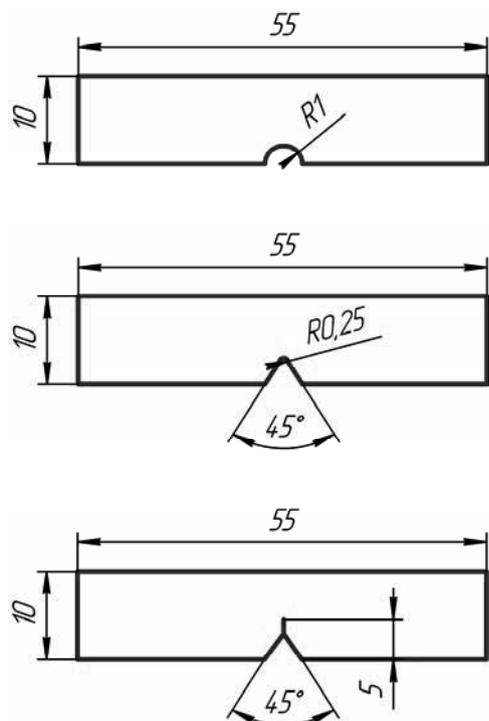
Образцы для испытаний на удар: а – U-образный надрез; б – V-образный надрез; в – образец с трещиной
